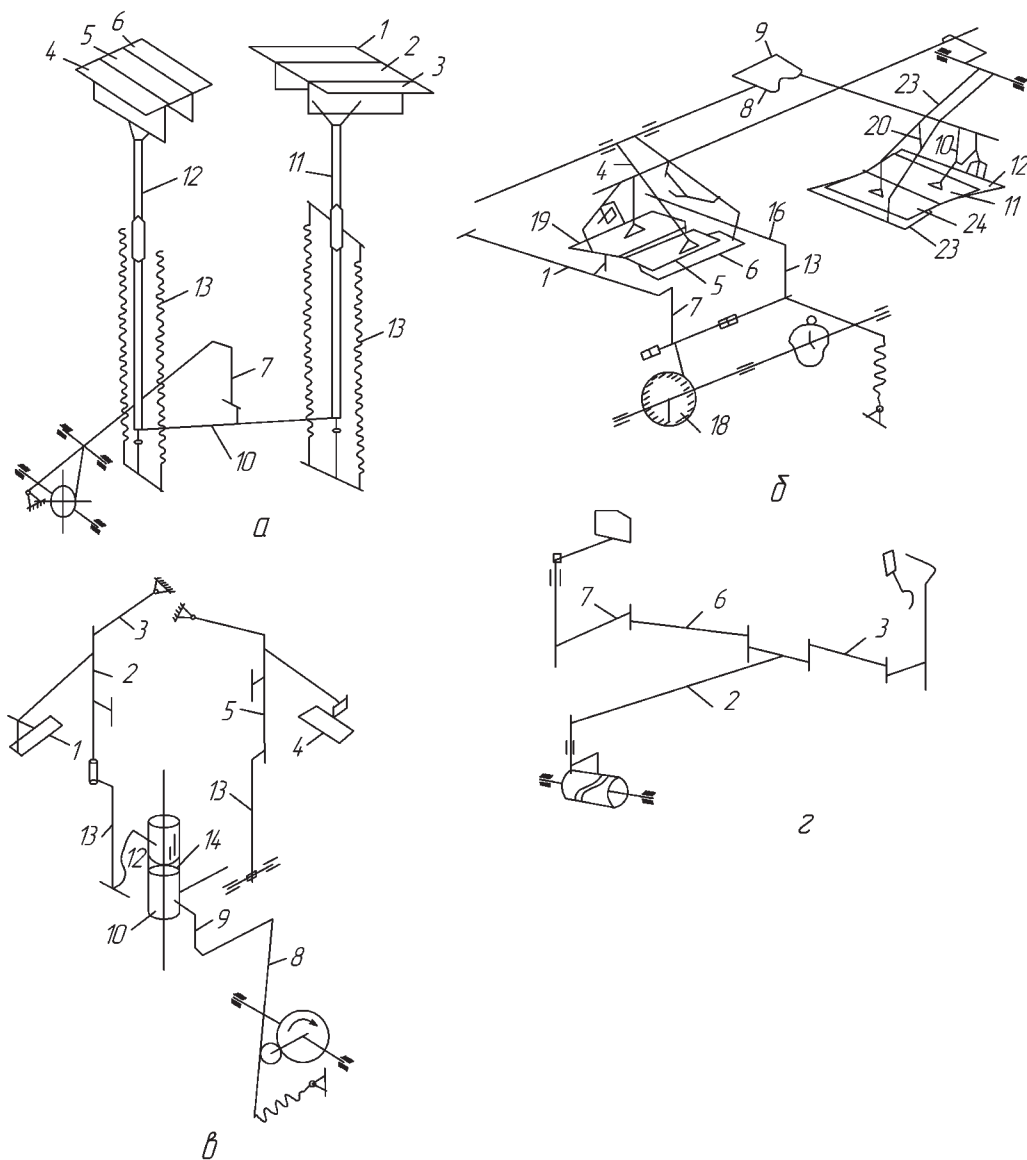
Механізми для формування внутрішнього й зовнішнього пакетів
